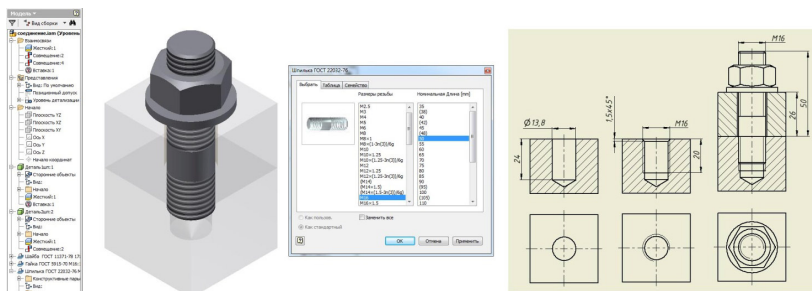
Сборка соединения шпилькой. Чертеж соединения
